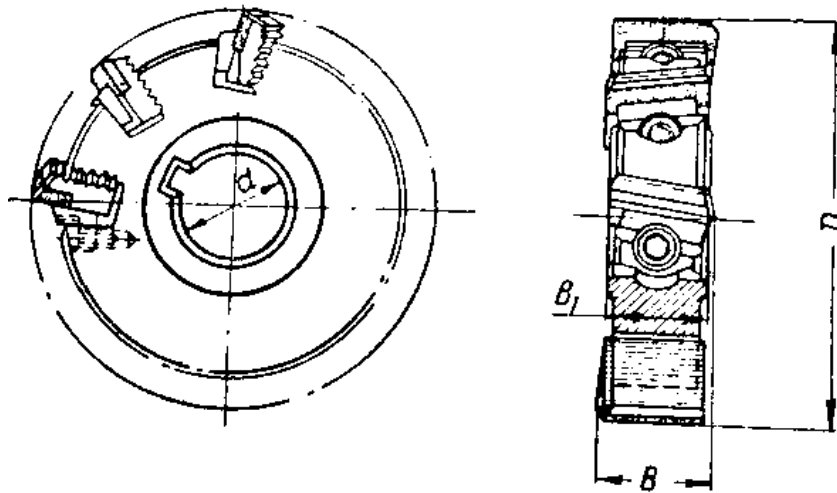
Дискова тристороння фреза із вставними ножами
